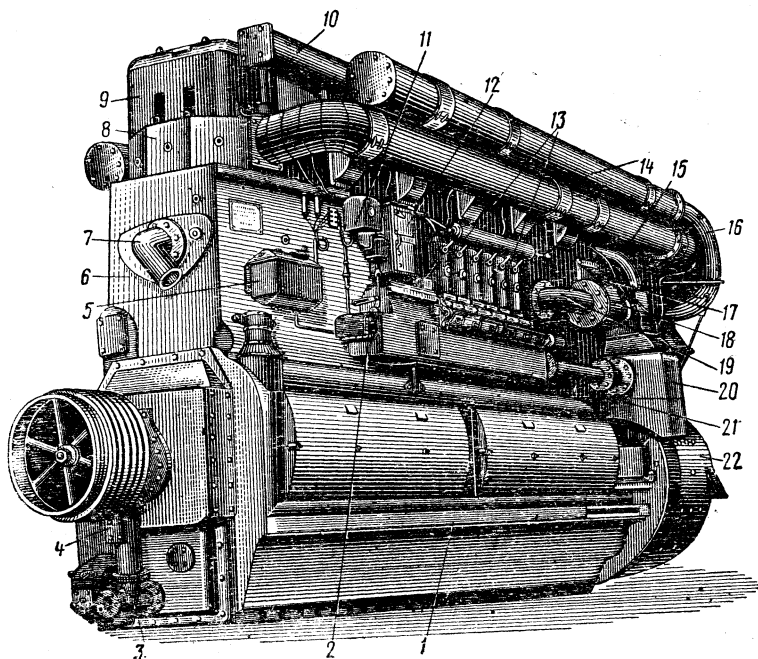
Общий вид дизеля 2Д50 со стороны топливного насоса; 1 — картер; 2 — электропневматический механизм; 3 — масляный насос; 4 — привод масляного насоса; 5 — фильтр тонкой очистки топлива; 6 — блок дизеля; 7 — патрубок подвода воды в блок; 8 — цилиндрическая крышка; 9 — клапанная коробка; 10 — водяной коллектор; 11 — катушка соленоида; 12 — регулятор числа оборотов; 13 — секции топливного насоса; 14 и 15 — выпускные коллекторы; 16 — турбовоздуходувка; 17 — нагнетательный патрубок водяного насоса; 18 — водяной насос; 19 — всасывающий патрубок водяного насоса; 20 — корпус приводных шестерен; 21 — картер топливного насоса; 22 — главный генератор
